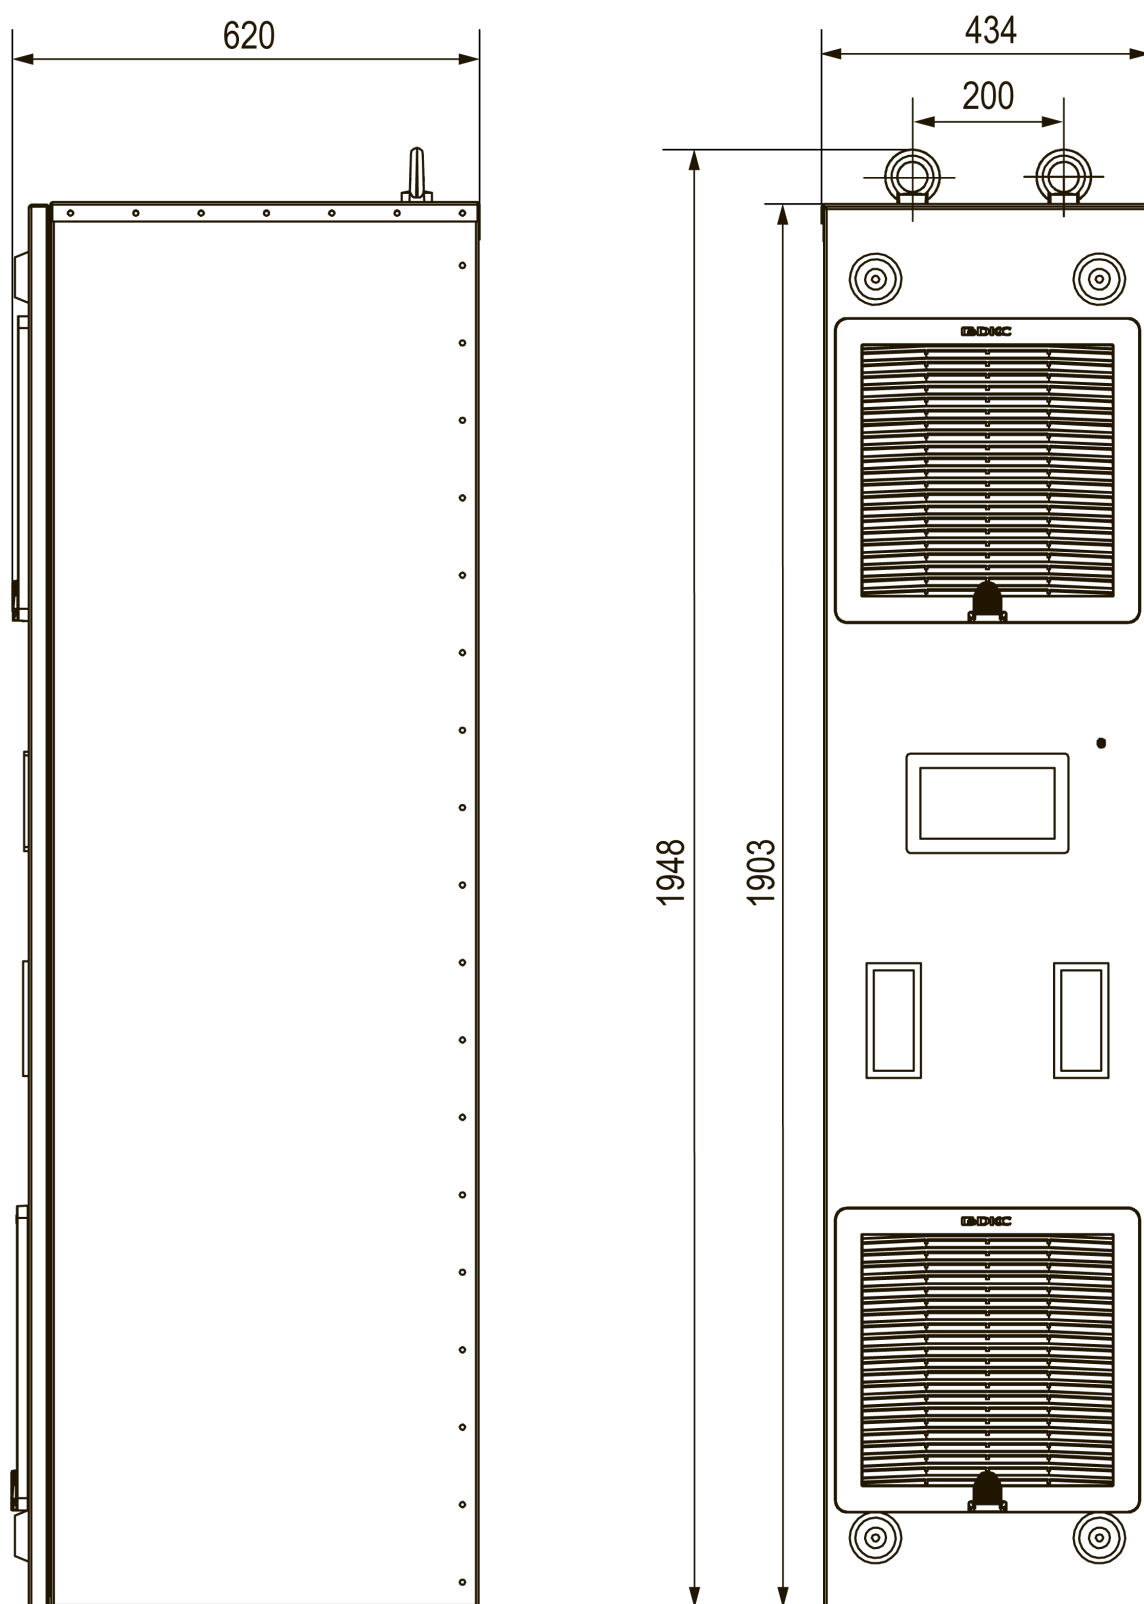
Габаритные размеры прибора в корпусе типоразмера 21
